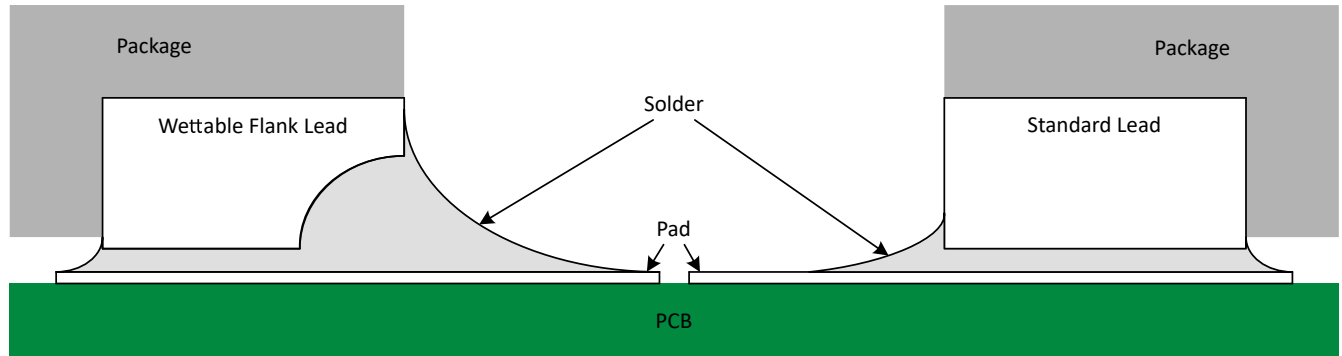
焊接后具有可润湿侧翼的 QFN 封装和标准 QFN 封装的简化剖面图
